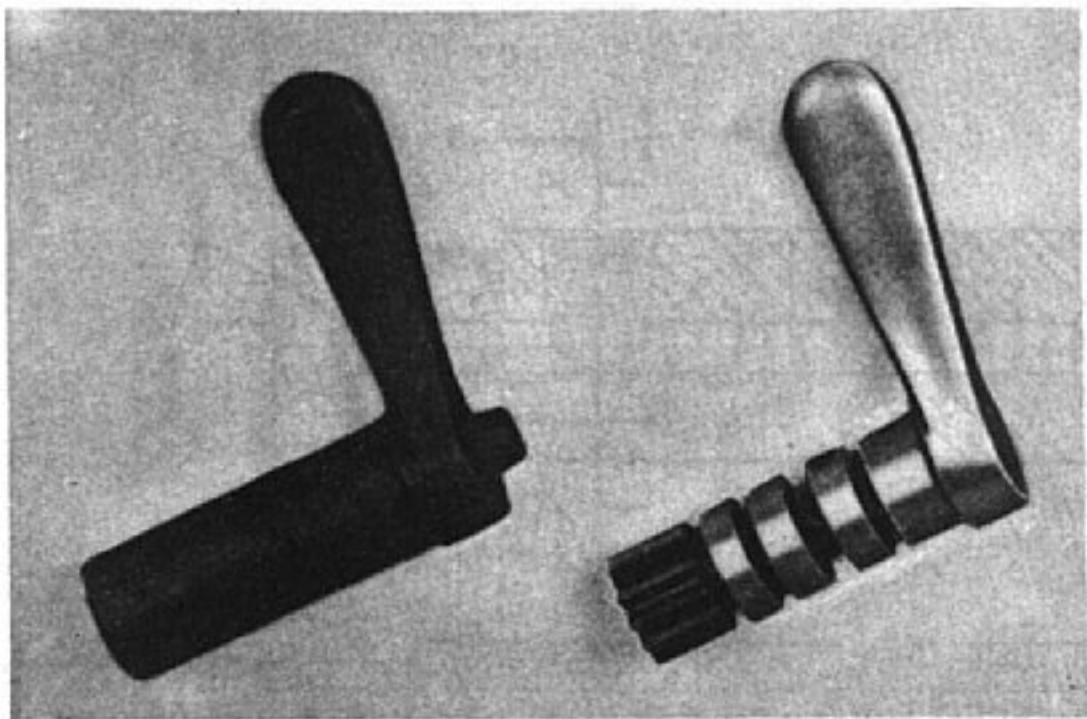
Manecilla operadora, antes y después de mecanizar. (The Hartford Special Machinery Company.)
